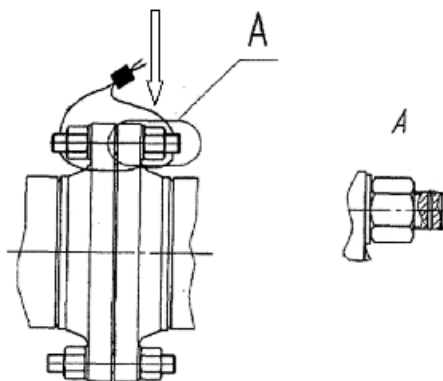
Места пломбировки фланцевых соединений калиброванного участка установок поверочных трубопоршневых Сапфир
